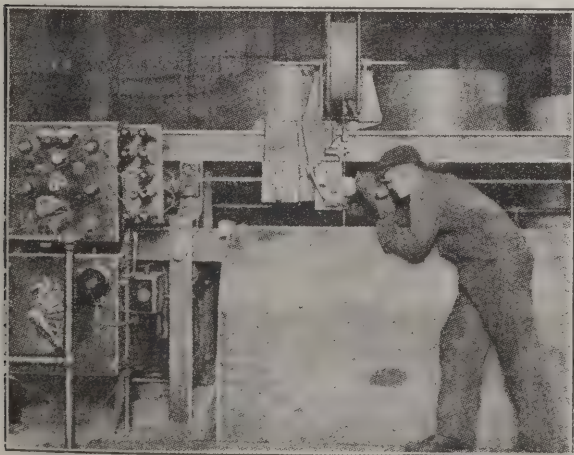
Soudure des côtés de gros réservoirs.
